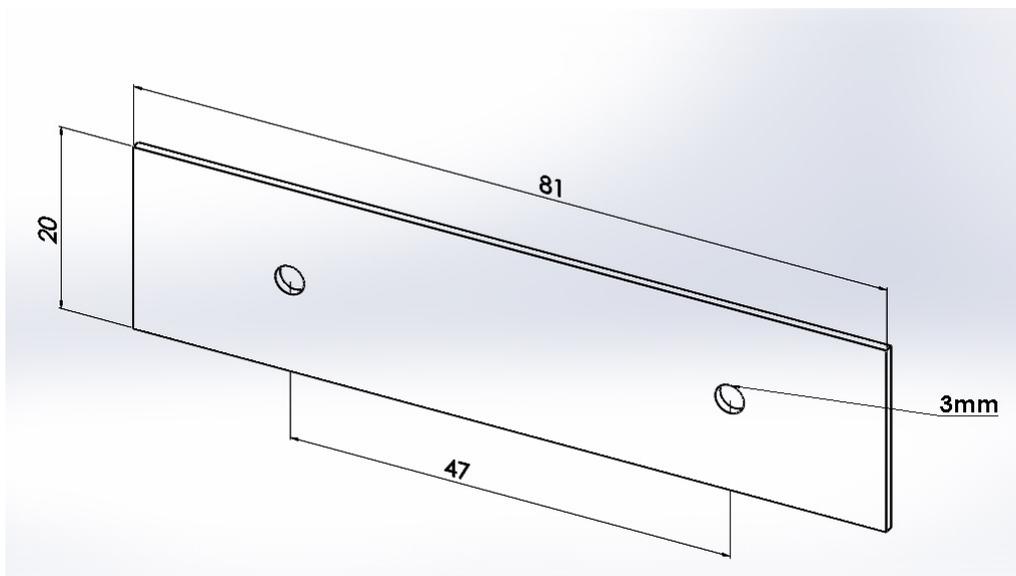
desenho técnico para auxiliar na construção do componente 4: placa fim de curso.
